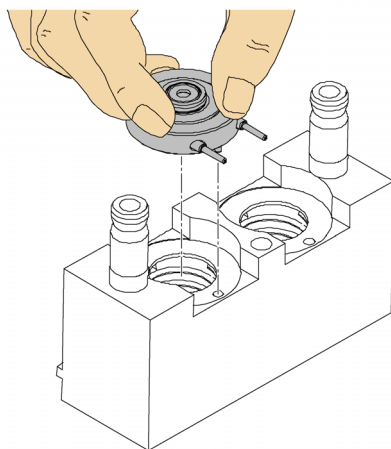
Insertion des bagues support de l'accessoire de rinçage de joint
